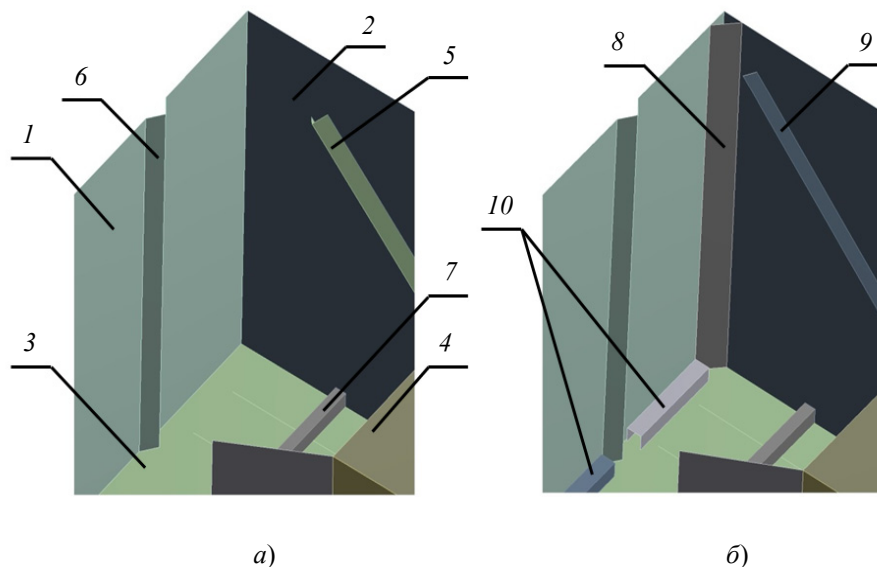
Фрагменты расчетных 3D моделей серийной (а) и модернизированной (б) цистерн пожарного автомобиля (вид изнутри угловых сварных соединений передней, боковой стенки и дна): 1 – передняя стенка; 2 – боковая стенка; 3 – дно; 4 – поперечный волнолом; 5 – ребро жесткости на боковой стенке; 6 – ребро жесткости на передней стенке; 7 – П-образный профиль; 8 – косынка; 9 – удлиненное ребро жесткости на боковой стенке; 10 – дополнительный П-образный профиль
